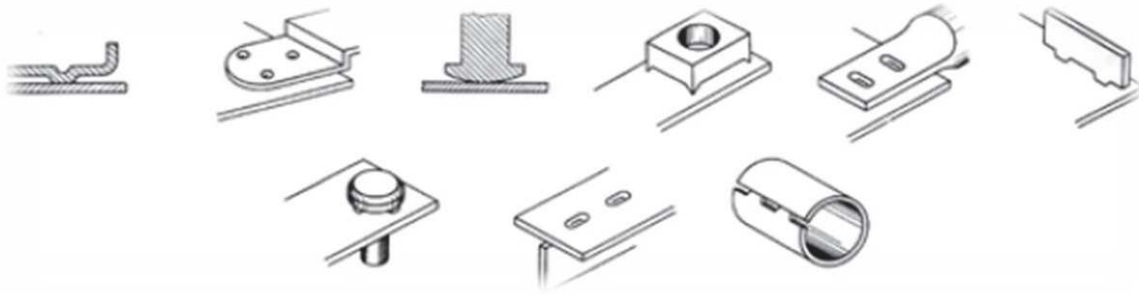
Soudage par bossages : assemblages typiques [8].
